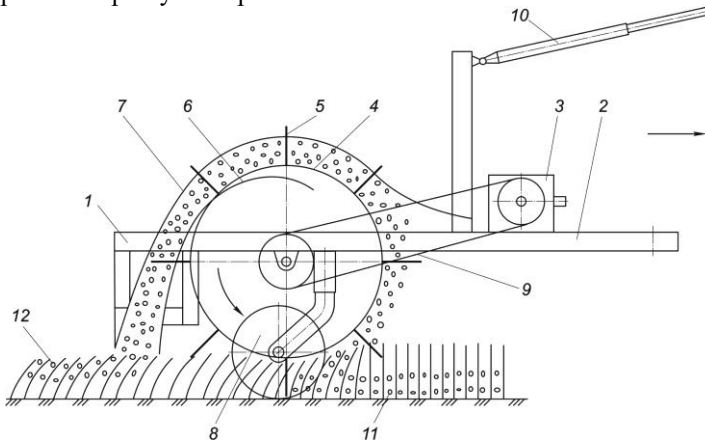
Схема машини для розпушування стеблової стрічки льону: 1 – рама; 2 – сниця; 3 – редуктор; 4 – диск; 5 – палець; 6 – напрямна поверхня; 7 – кожух; 8 – самоустановлювальні колеса; 9 – привод; 10 – гідроциліндр; 11, 12 – стеблова стрічка льону, відповідно, до і після розпушування
